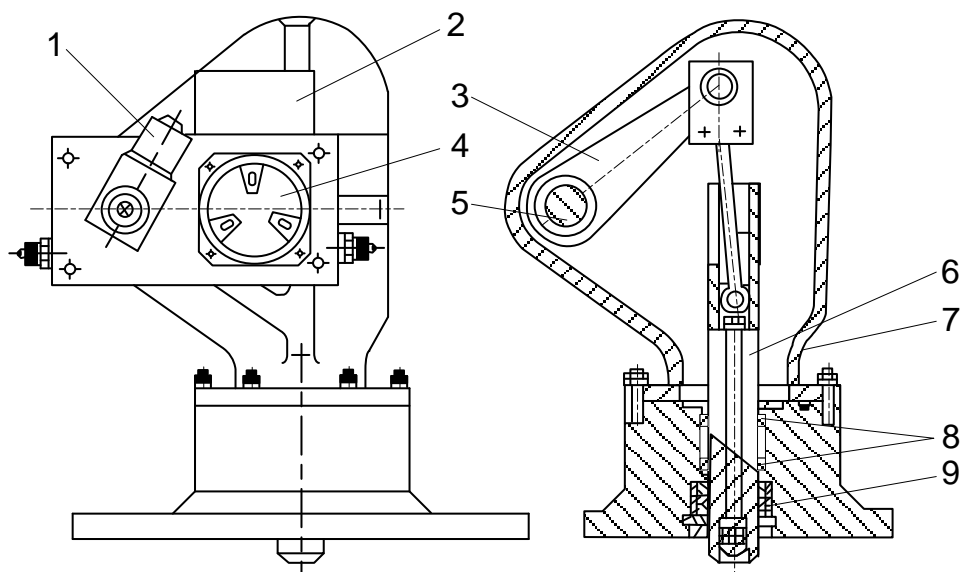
Елегазовий заземлювач: 1 - блок-замок; 2 — блок комутуючих контактів; 3-механізм підйомний; 4 — показчик положення заземлювача; 5-вал; 6 — стрижень що заземлює; 7 — корпус; 8 — напрямні; 9 - контакти струмоз'ємні
